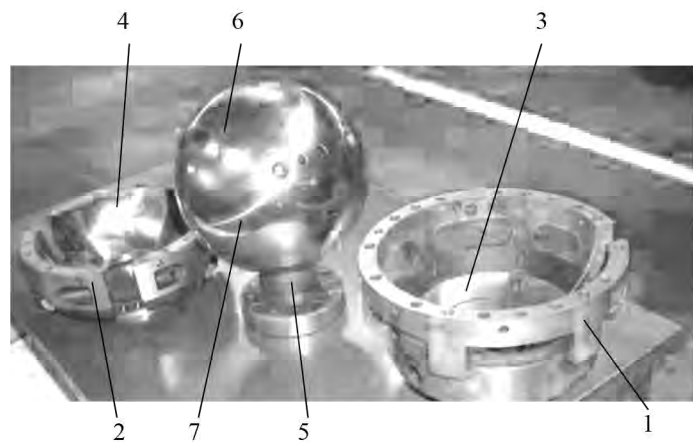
Основні деталі виготовленого опорного вузла та ділянки точних сферичних поверхонь деталей
